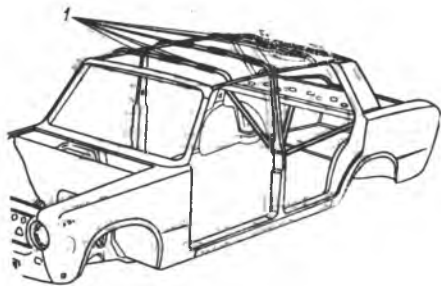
Установка прокладок типа «Келлер» (I) на усилители крыши
